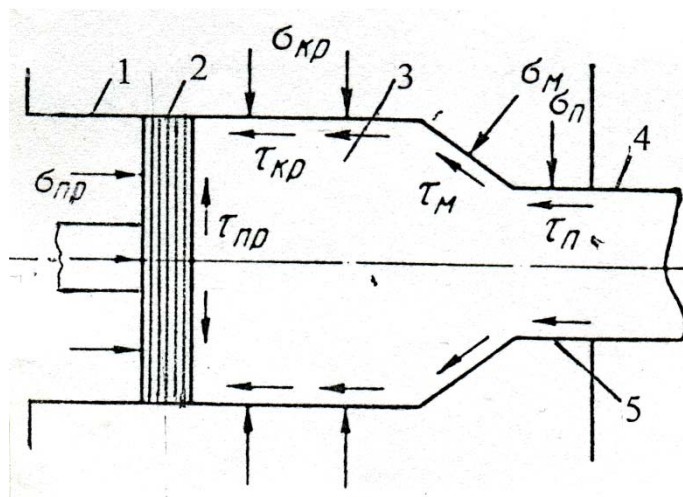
Напруження на контакті от зовнішніх сил P і T , які діють на метал при пресуванні з прямим витіканням: 1 - контейнер; 2 - плунжер; 3 - заготовка; 4 - готовий виріб; 5 - калібруючий поясочок
